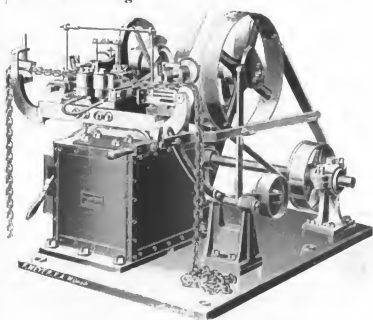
Elektrische Kettenschweißmaschine.
